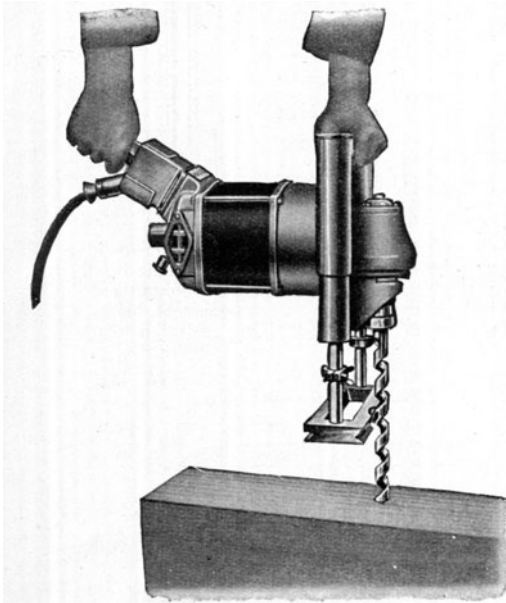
Handmaschine wie Abb. 55, zum Bohren eingerichtet. Die gleiche Maschine kann auch als Abläng-Kettensäge (ähnlich Abbildung 56) verwendet werden.
